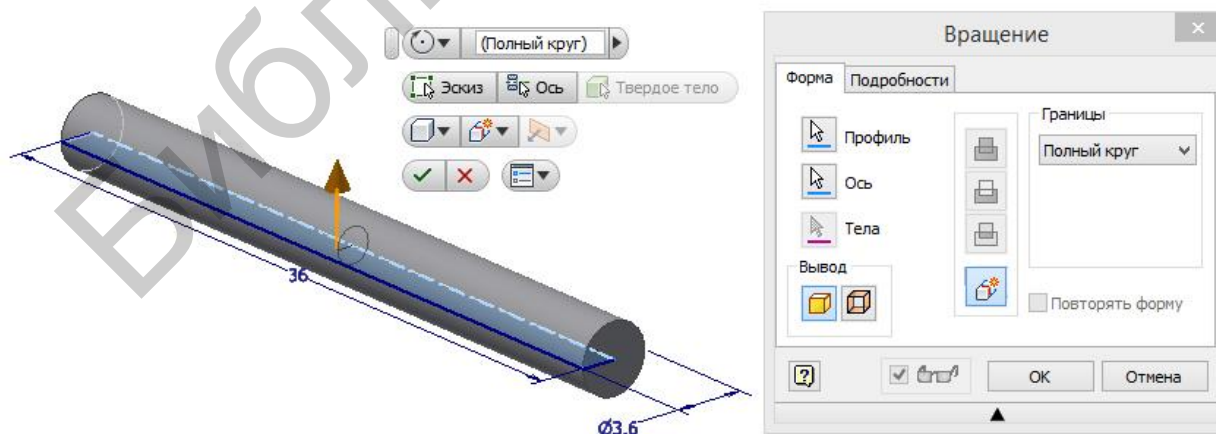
Первая стадия построения модели детали «Контакт» – получение цилиндрической заготовки
